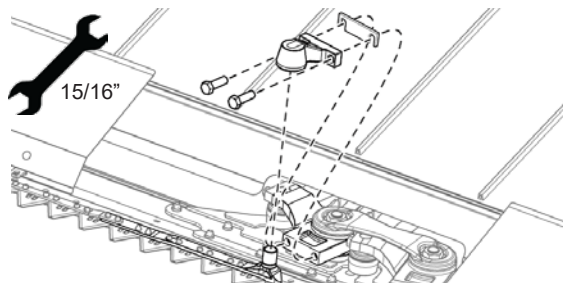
Снятие корпуса подшипников с головки правого ножа
